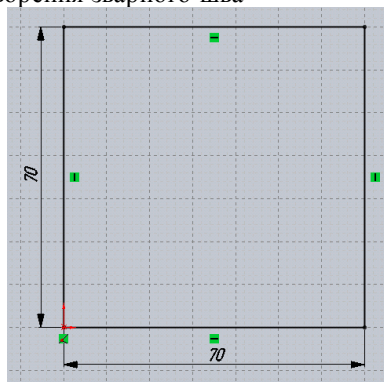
Ескіз для напускного зварного з'єднання
